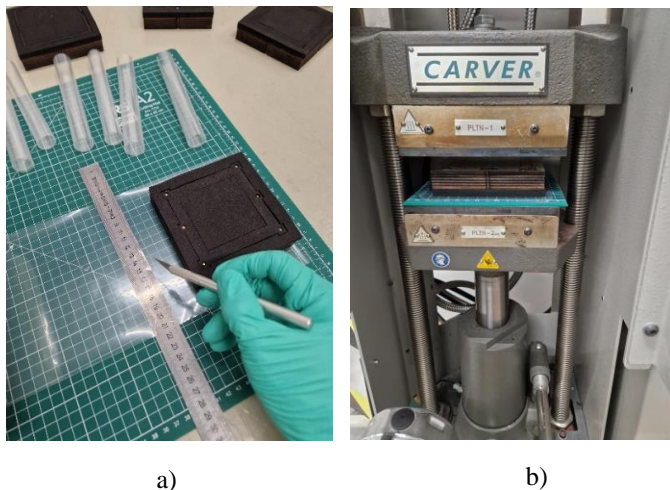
Découpe au scalpel d'un carré large de sous-joint (a) et découpe d'un sous-joint à l'aide d'un emporte-pièces et sous presse (b)
